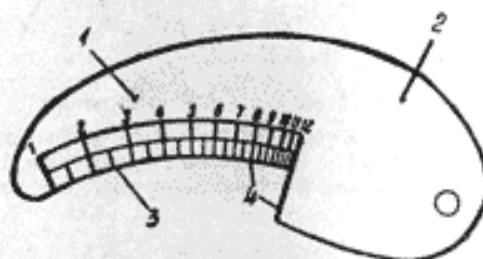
Шаблон для проверки формы и размеров клепки остива:
